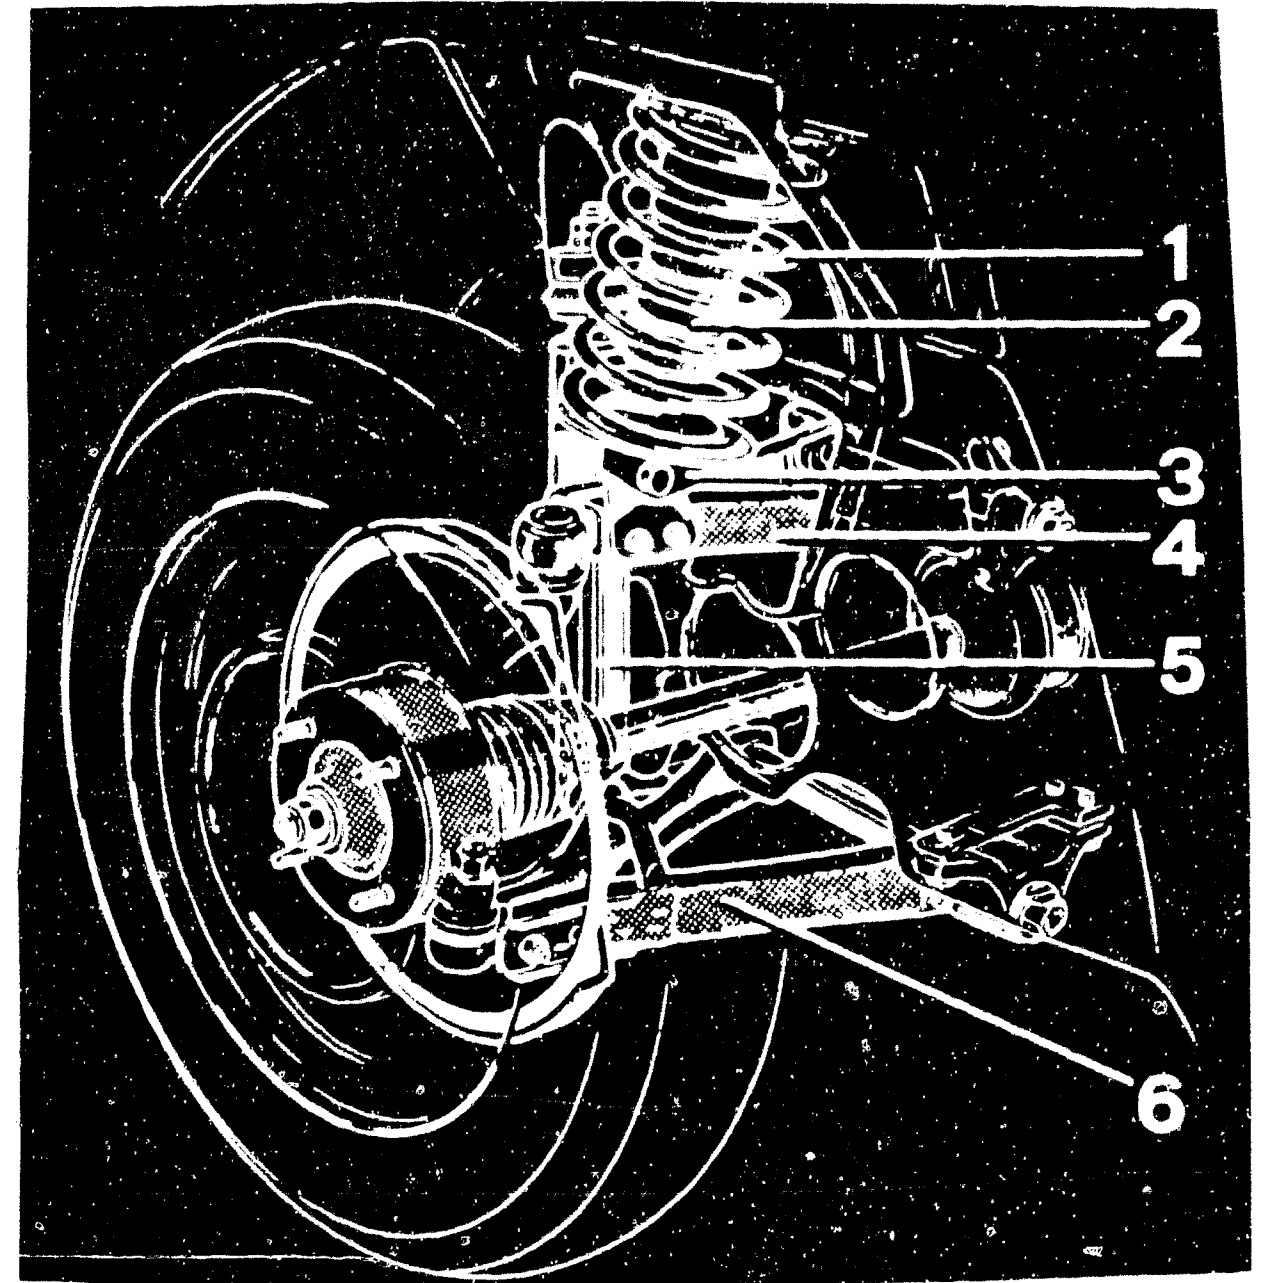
Vorderradaufhängung: 1 Schraubenfeder – 2 Anschlagpuffer – 3 Unterer Federsitz – 4 Oberer Querlenker – 5 Stossdämpfer – 6 Unterer Querlenker.
